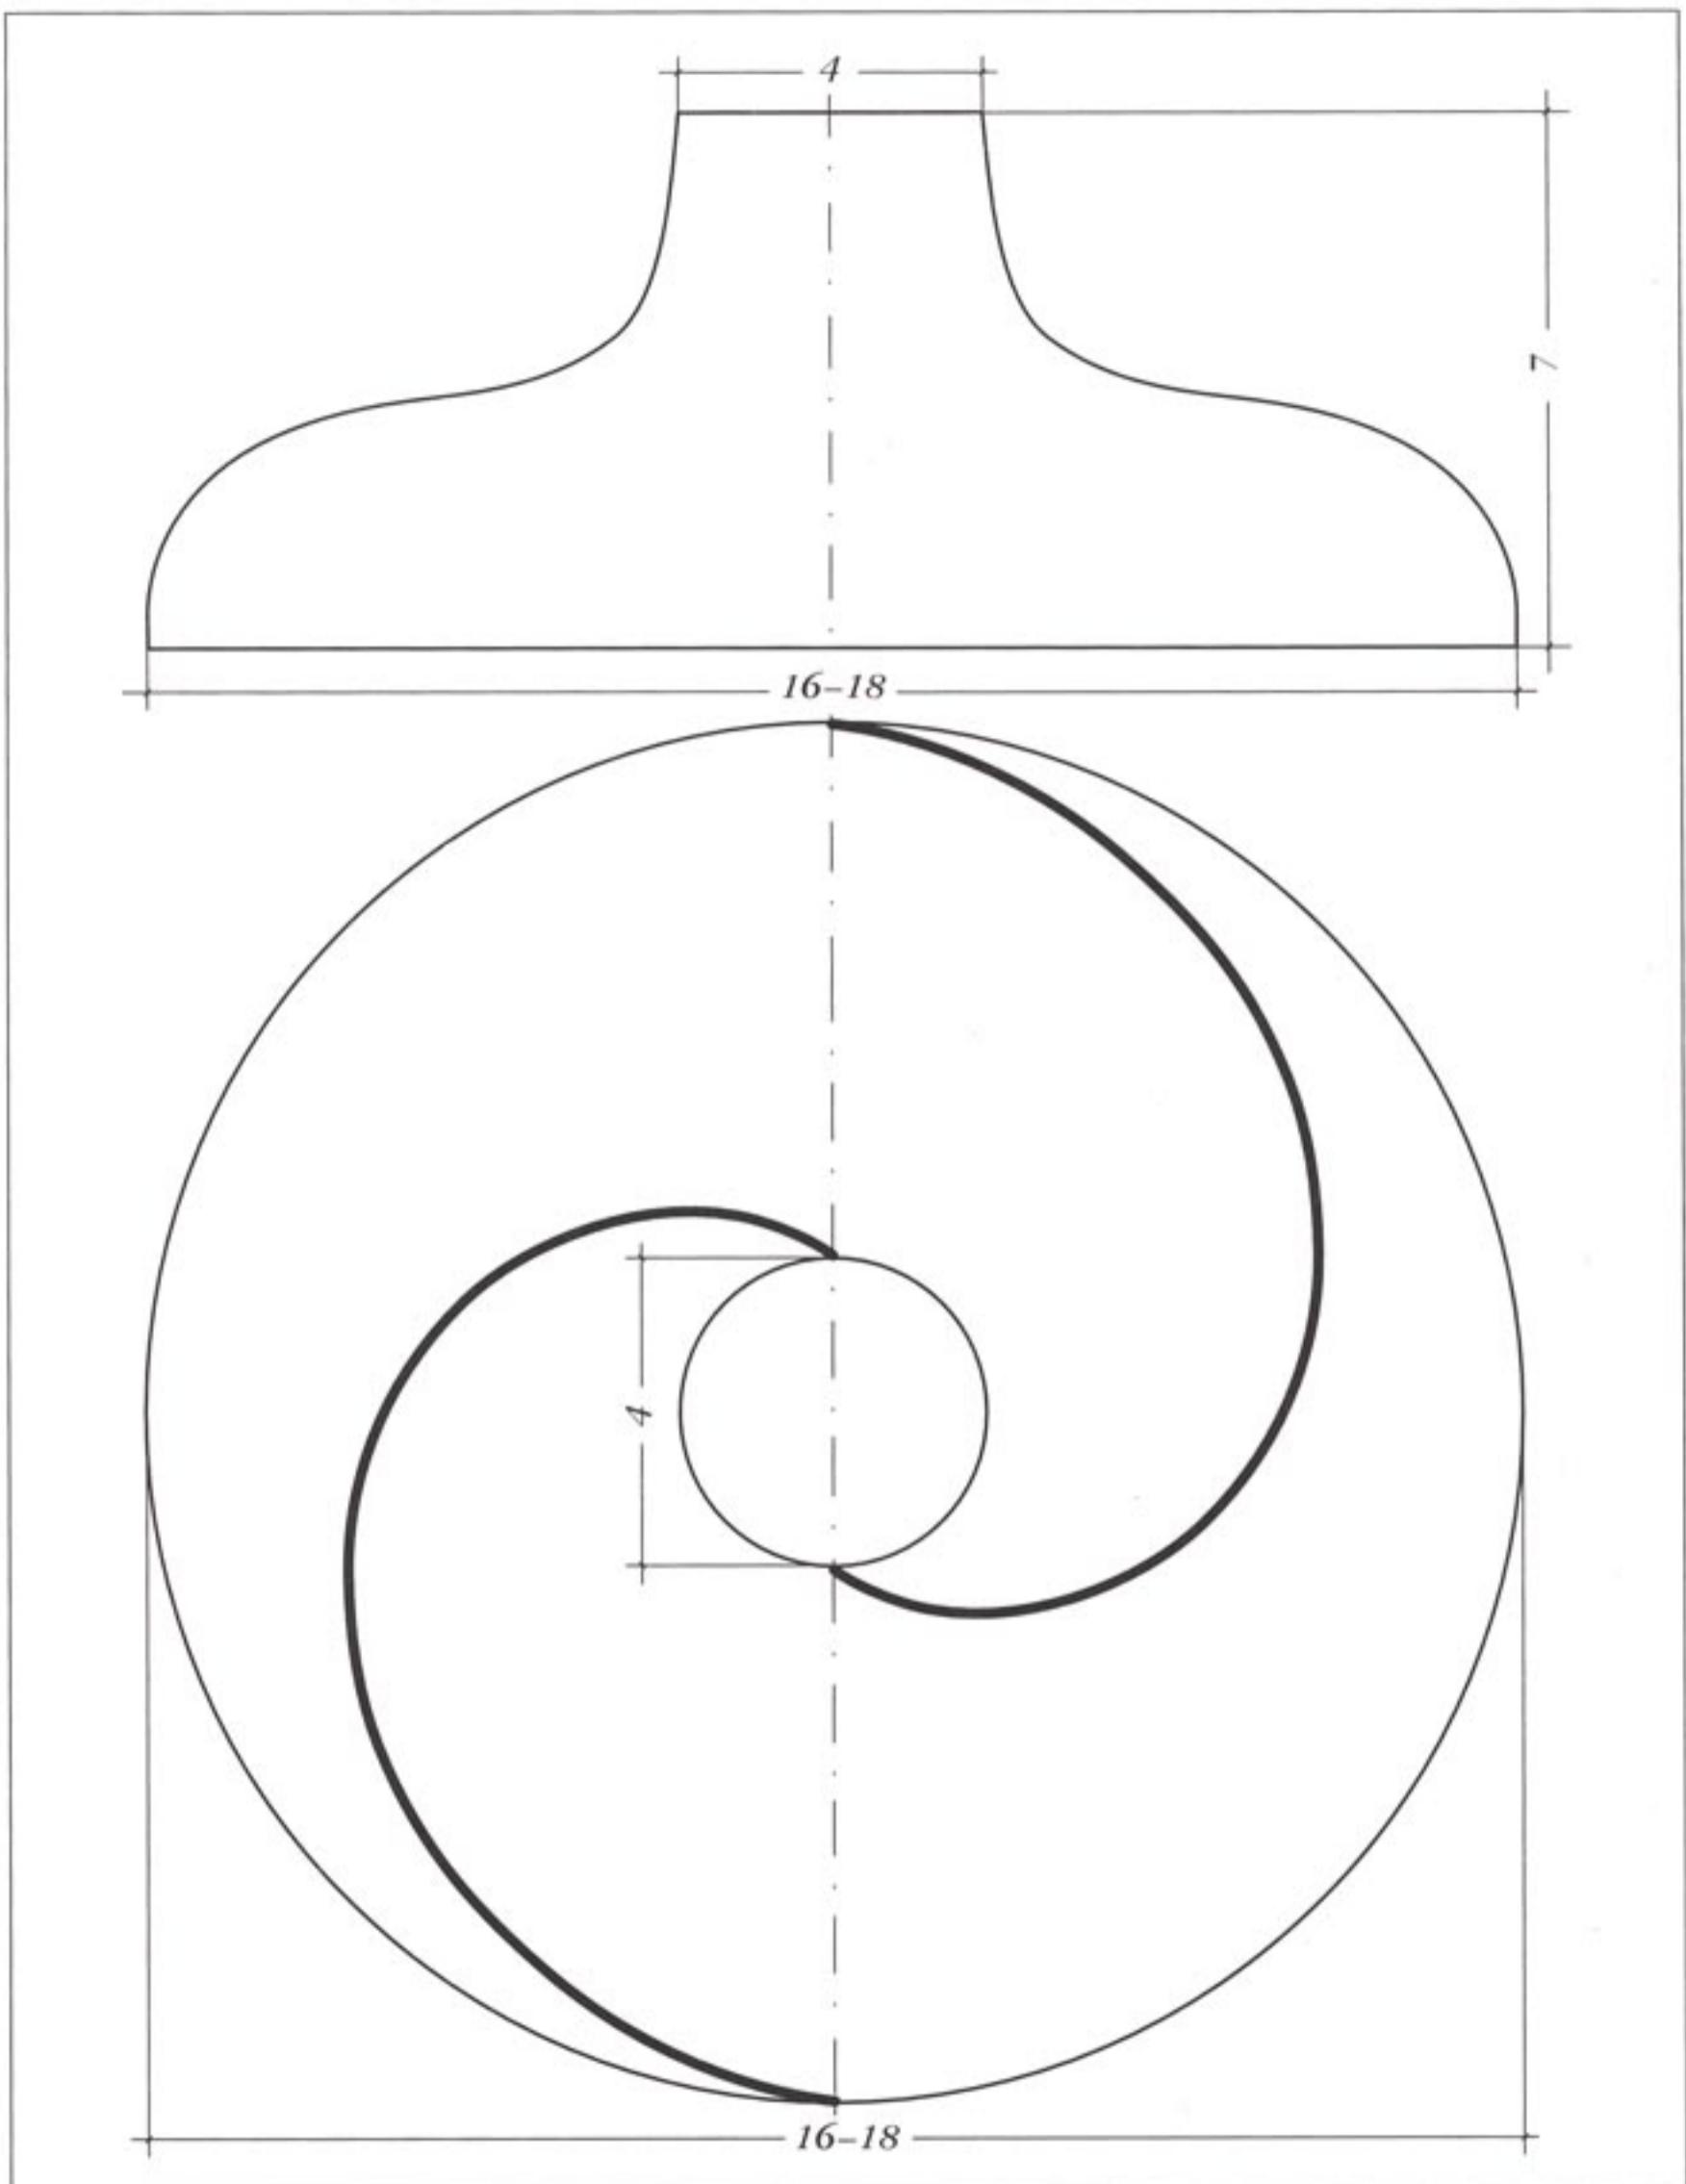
Чертеж и схема разметки стойки трехсвечника к рис. 181
